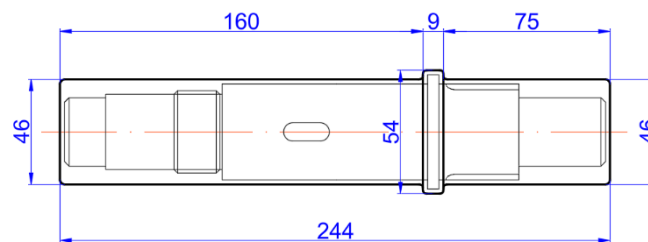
Ескіз деталі вал ступеневий з контуром заготовки
